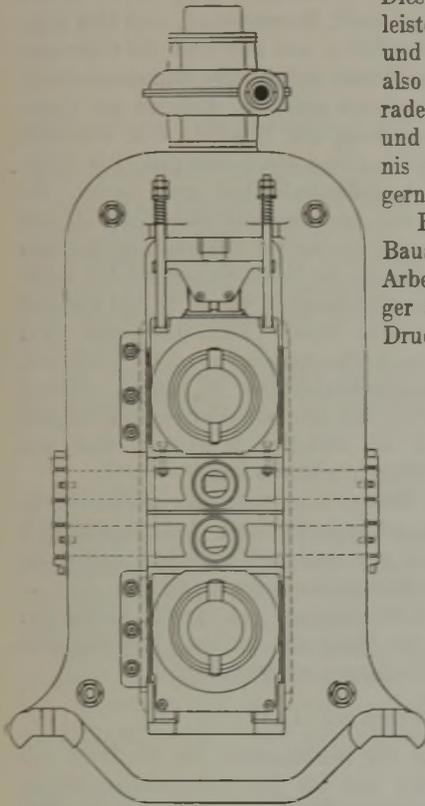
Blechwalzgerüst mit Rollenlagern an den Arbeits- und Stützwalzen.
